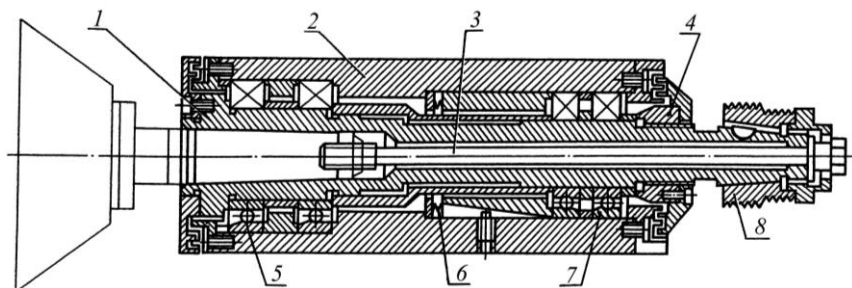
Головка шлифовальная универсально-заточного станка модели 3Д642Е
